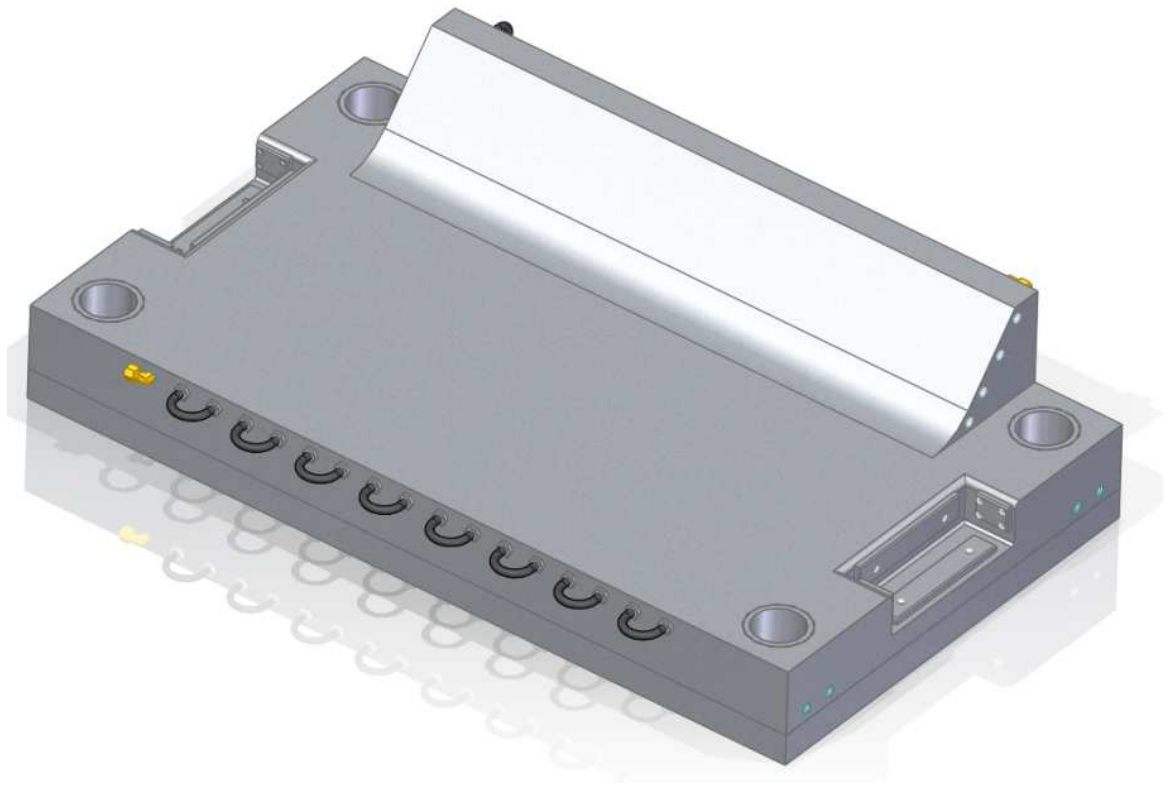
Výrobek pro technologii Crush-Core – pohled 2
